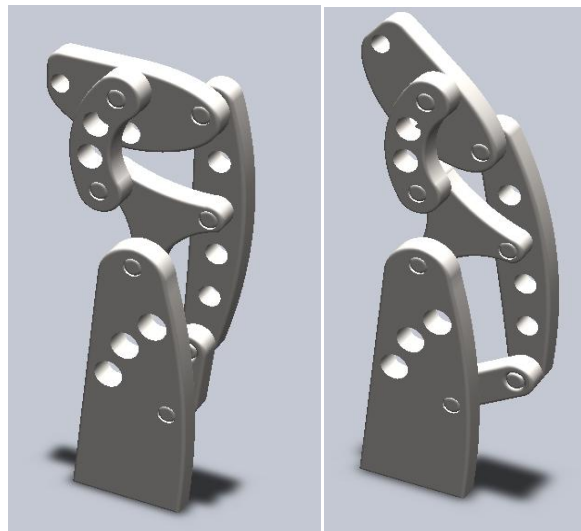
mecanismo de barras modelado en solidworks©, (a) posición de la rodilla a 90° grados, (b) posición de rodilla en extensión de 15°.
